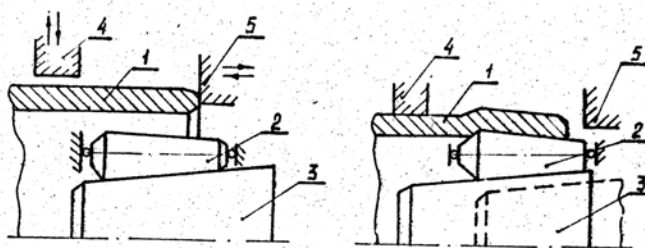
Схема внутренней раскатки концов труб: 1 – труба; 2 - деформирующий ролик; 3 - опорный ролик; 4 – зажим; 5 - упор
